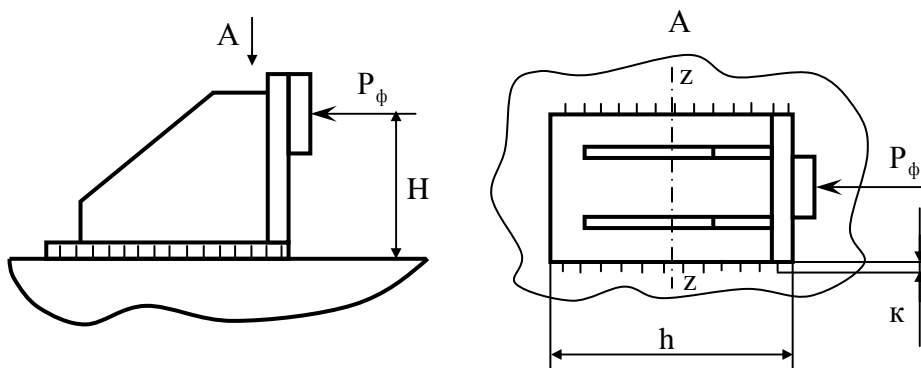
Розрахункова схема закріплення упора зварними швами
